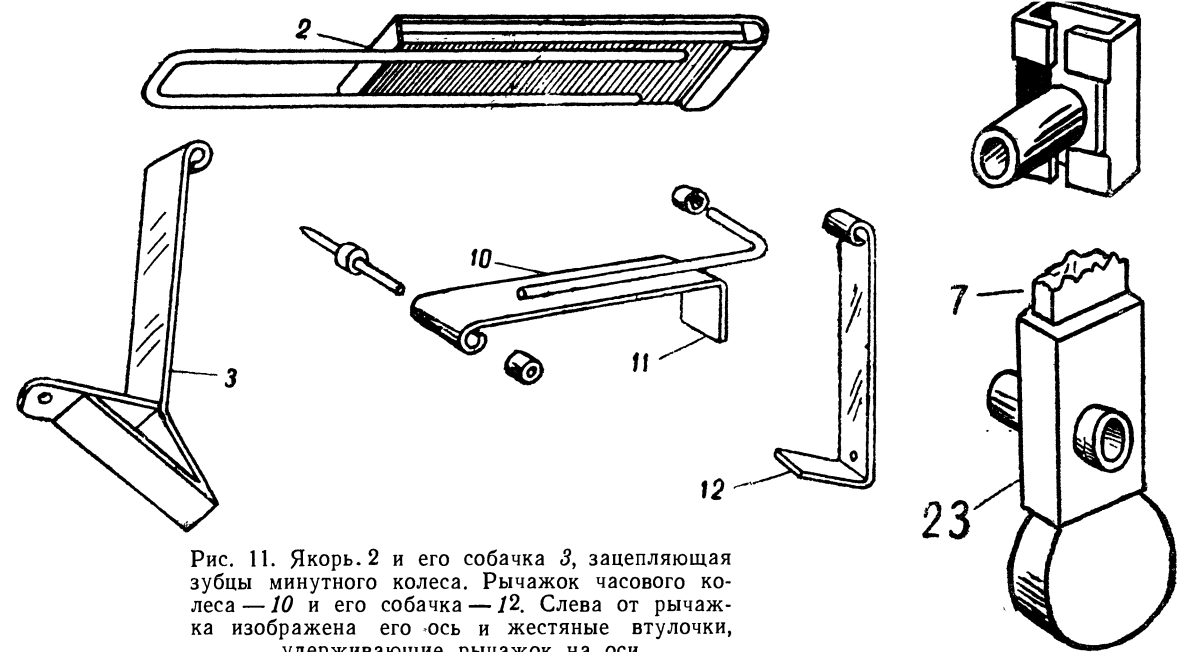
Якорь 2 и его собачка 3, зацепляющая зубцы минутного колеса. Рычажок часового колеса — 10 и его собачка — 12. Слева от рычажка изображена его ось и жестяные втулочки, удерживающие рычажок на оси
